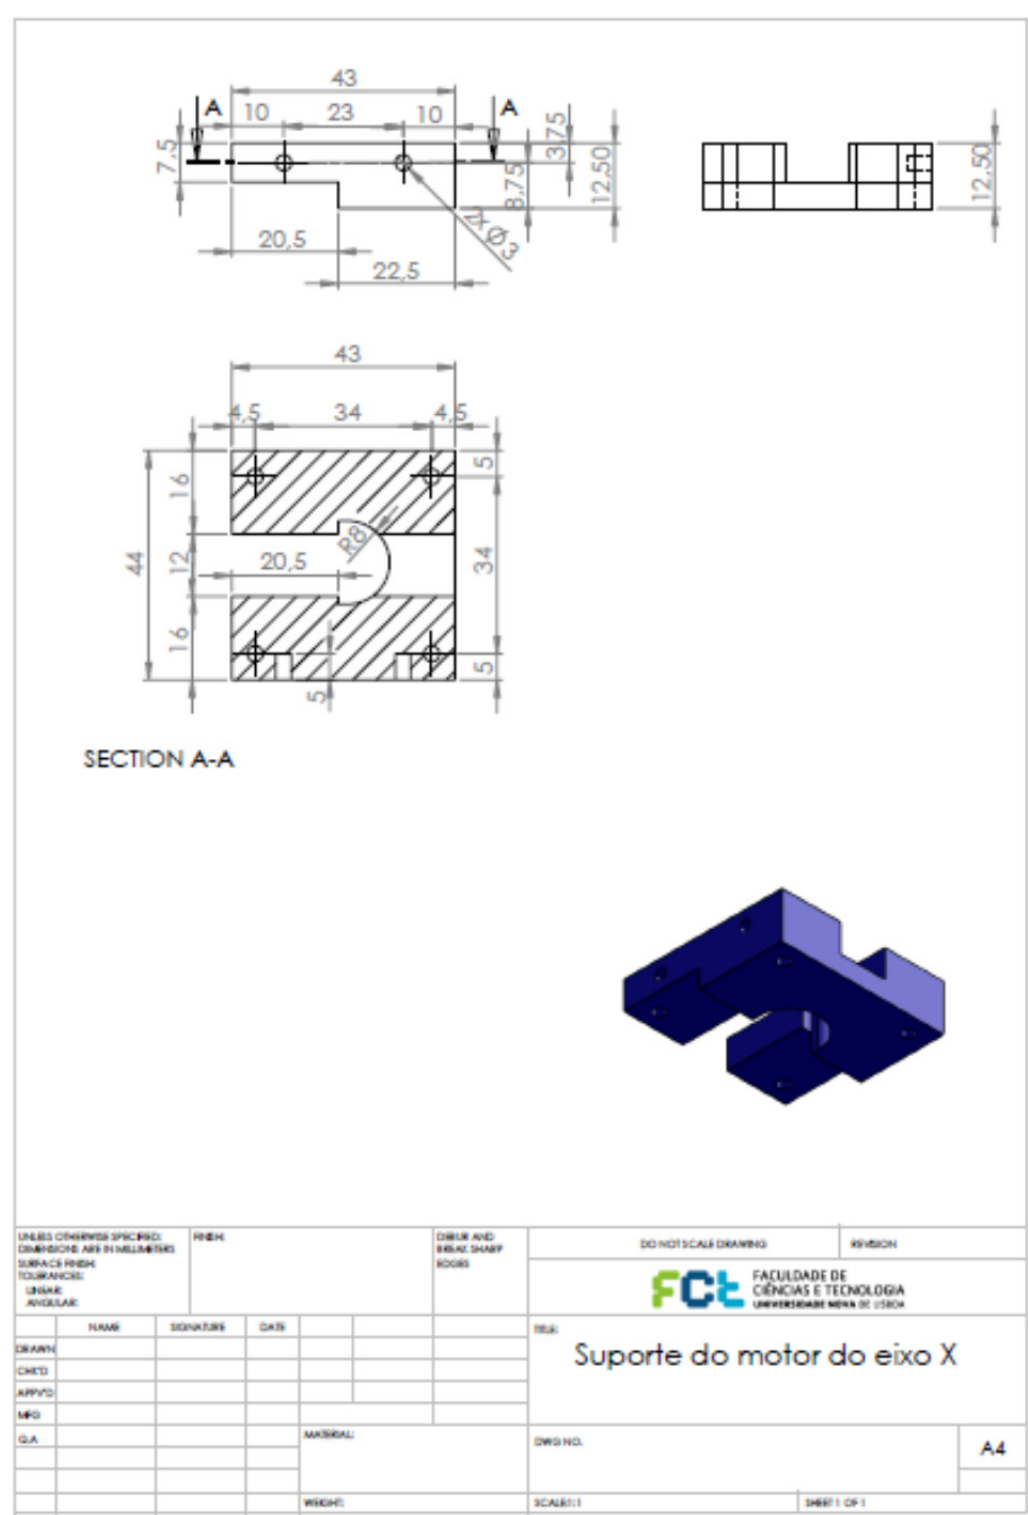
desenho técnico do suporte do motor do eixo X.
